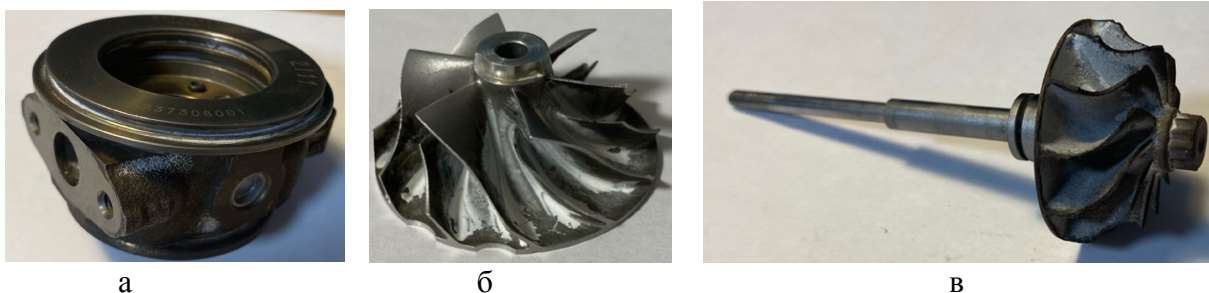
Исходные детали турбокомпрессора: а – корпус, б – колесо, в -вал
